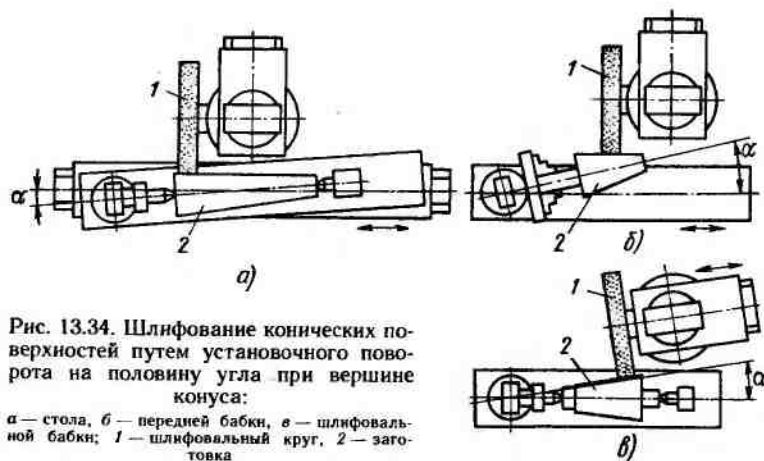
Шлифование конических поверхностей путем установочного поворота на половину угла при вершине конуса:
